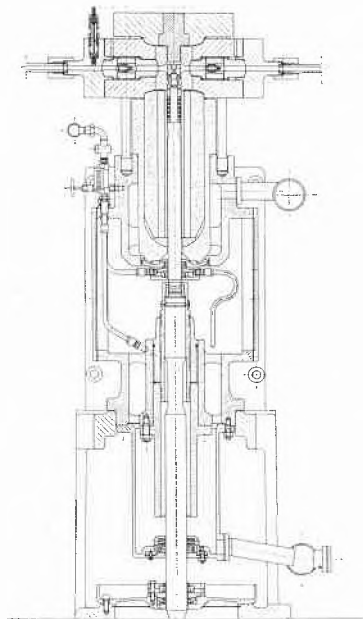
Großkompressor für 2000 at, Kolbendurchmesser 45 mm. Kerbwirkung der Durchdringung im Ventilkopf, kompensiert durch Schrumpfung
